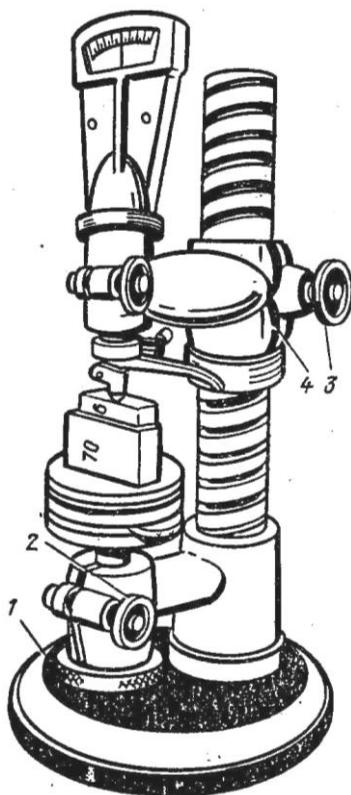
Установка на размер прибора с тяжелой стойкой
